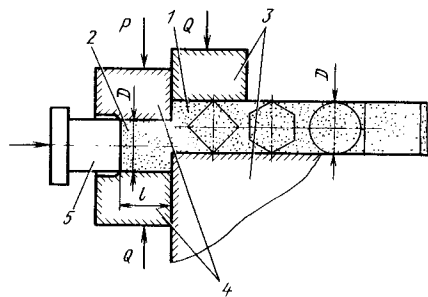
Схема чистой резки полосы или прутка различного сечения:
